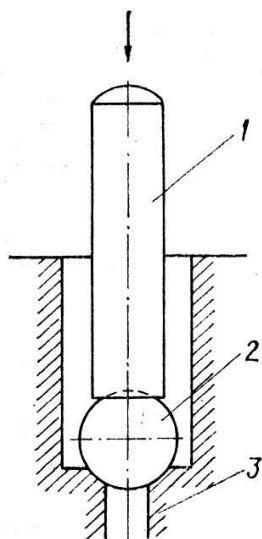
Схема об-пресування кулькою клапанного гнізда:
